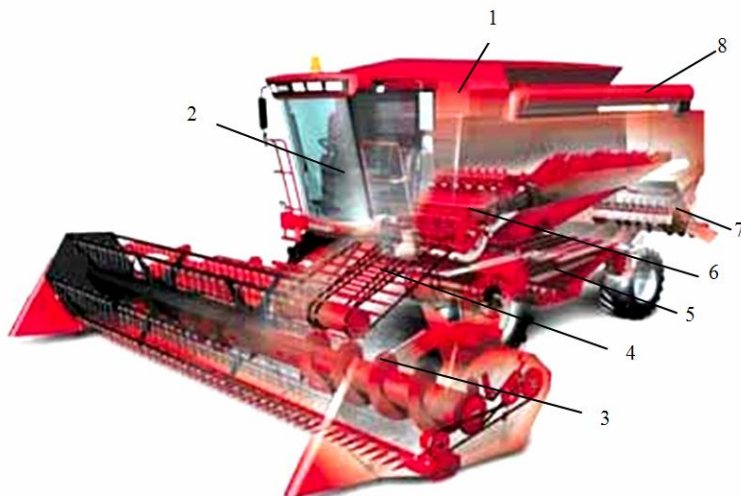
Зерноуборочный комбайн «Лидя-1600»:
